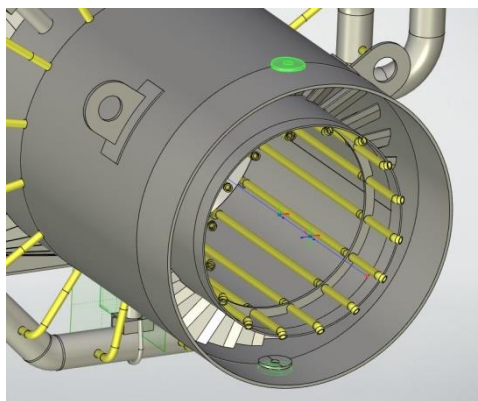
Новая конструкция крепления поворотной насадки
